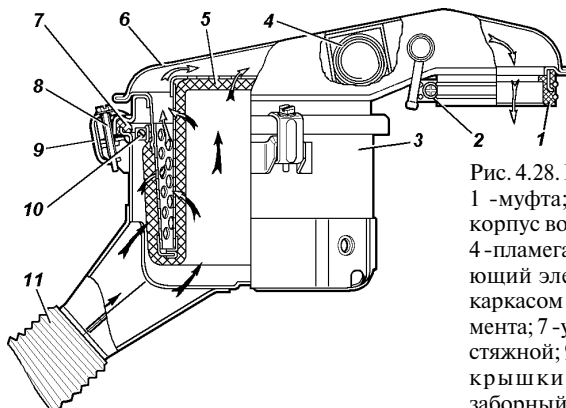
Воздушный фильтр: 1 - муфта; 2, 10 - хомуты; 3 - корпус воздушного фильтра; 4 - пламегаситель; 5 - фильтрующий элемент; 6 - крышка с каркасом фильтрующего элемента; 7 - уплотнитель; 8 - болт стяжной; 9 - скоба крепления крышки; 11 - воздухозаборный рукав
